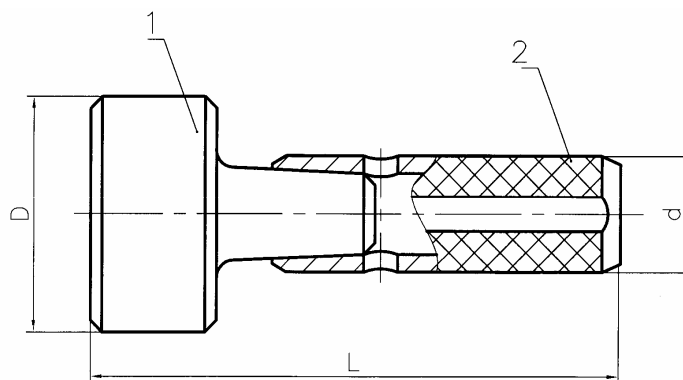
Гладкий непроходной калибр-пробка с неполной вставкой:
